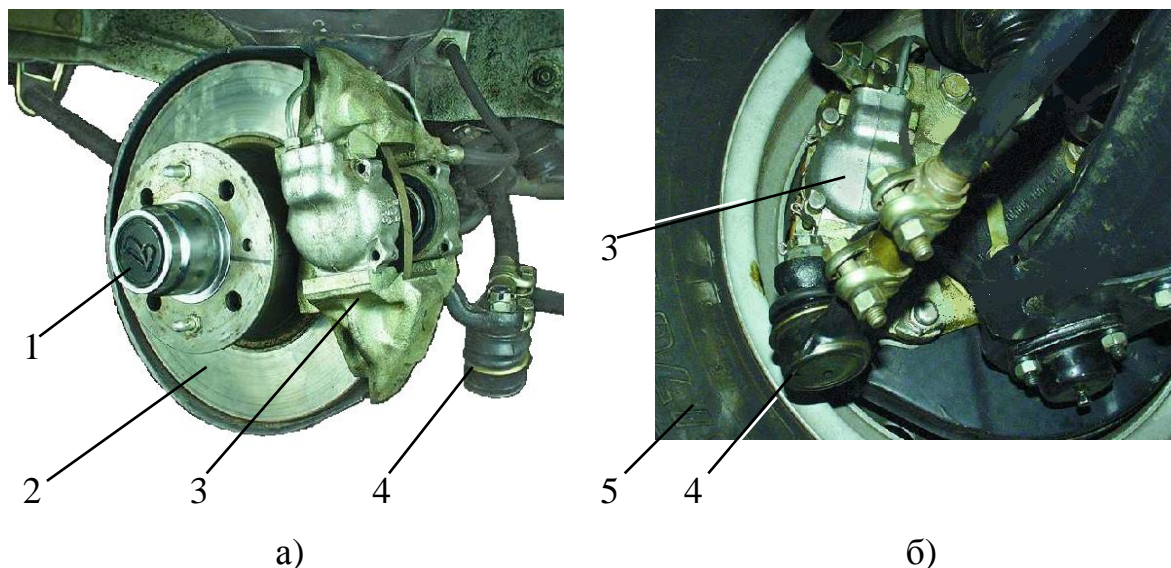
Дисковый тормозной механизм с фиксированной скобой: а – вид снаружи, б – вид изнутри; 1 – ступица колеса; 2 – тормозной диск; 3 – суппорт в сборе; 4 – шарнир рулевой тяги; 5 – колесо
